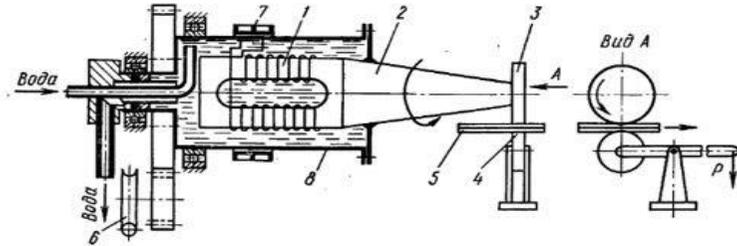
Схема установки для роликовой (шовной) сварки ультразвуком состоит из [5]: 1 – электромеханического преобразователя; 2 – трансформатора упругих колебаний; 3 – сваривающего ролика; 4 – прижимного ролика; 5 – изделия; 6 – механизма привода; 7 – подвода тока от ультразвукового генератора; 8 – кожа преобразователя.
